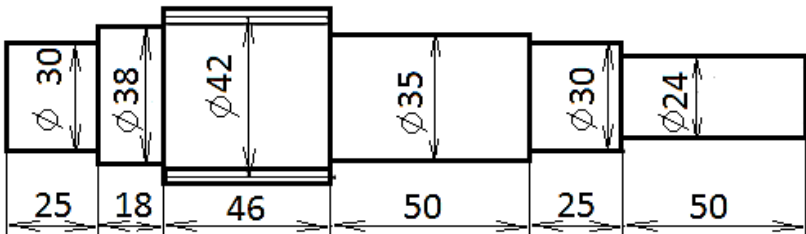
Вал 4 револьверної головки (рис. 7.1)
